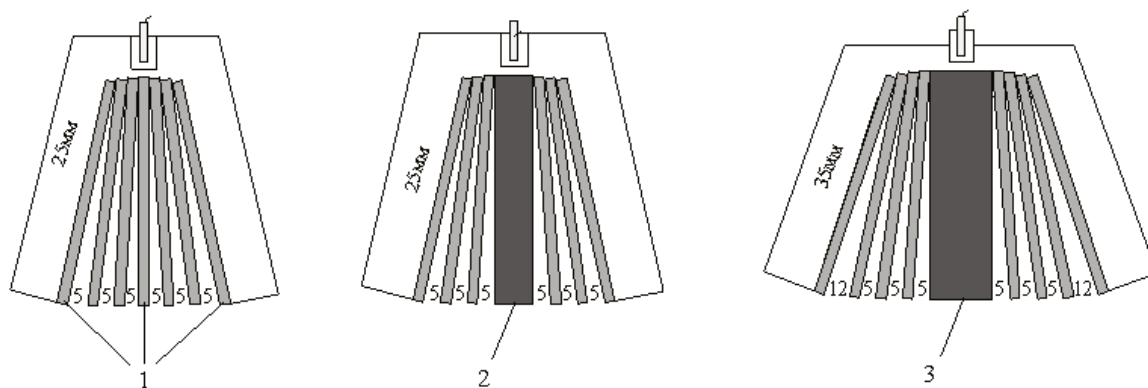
Схема сварки взрывом многослойной композиции, проходящей в 3 этапа
